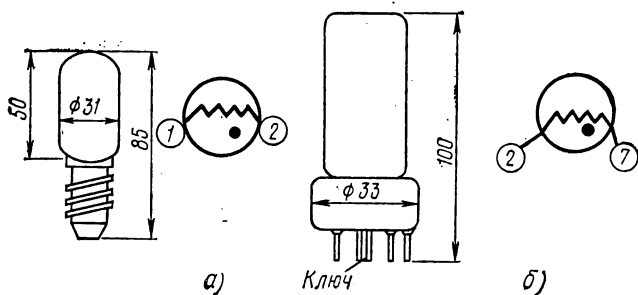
Габаритные чертежи и цоколевка бареттеров:
